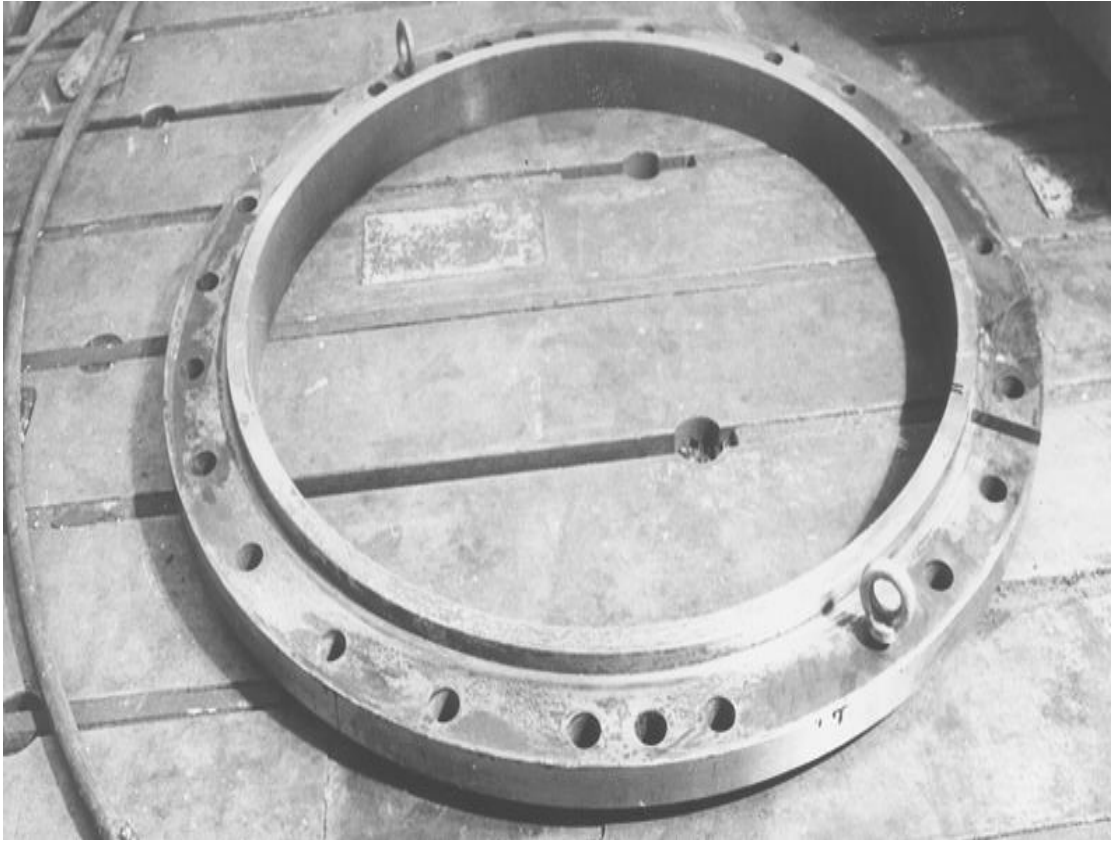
Жорстке колесо хвильової зубчастої передачі редуктора приводу нахилу міксеру МП – 600АС з локалізованим контрольним зубцем
